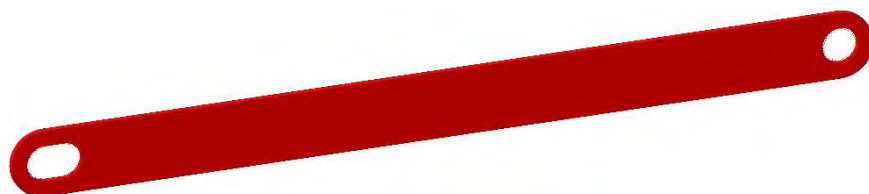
Фиксатор для блокировки гидроцилиндра
